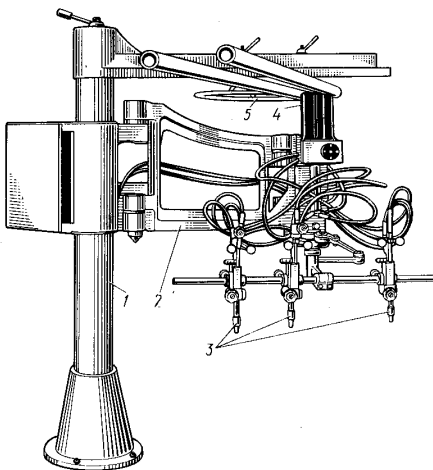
Общий вид шарнирной машины АСШ-70:
